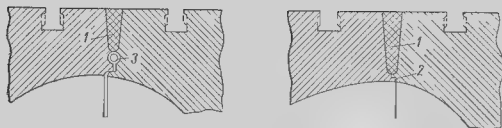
Конструкция сварного шва в роторах турбин ББЦ: а — первоначальная; б — современная
